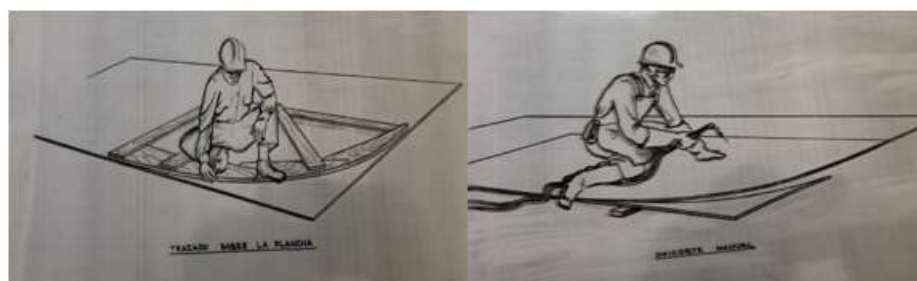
Trazado y corte Manual de Piezas con apoyo de Plantillas
